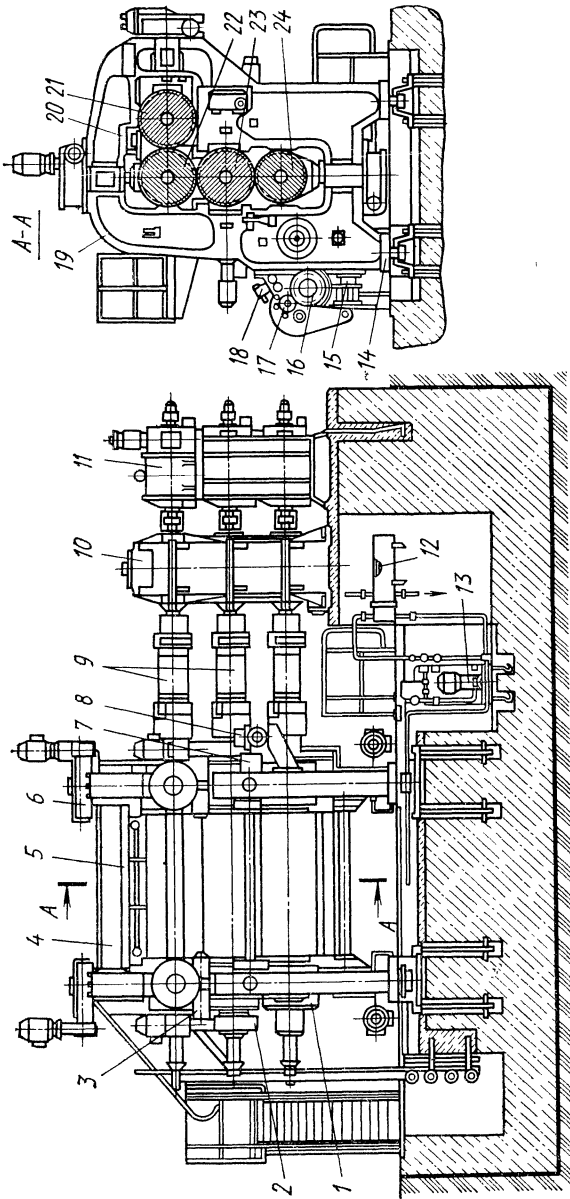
Четырехвалковый Г-образный калаандр 710×1800:
